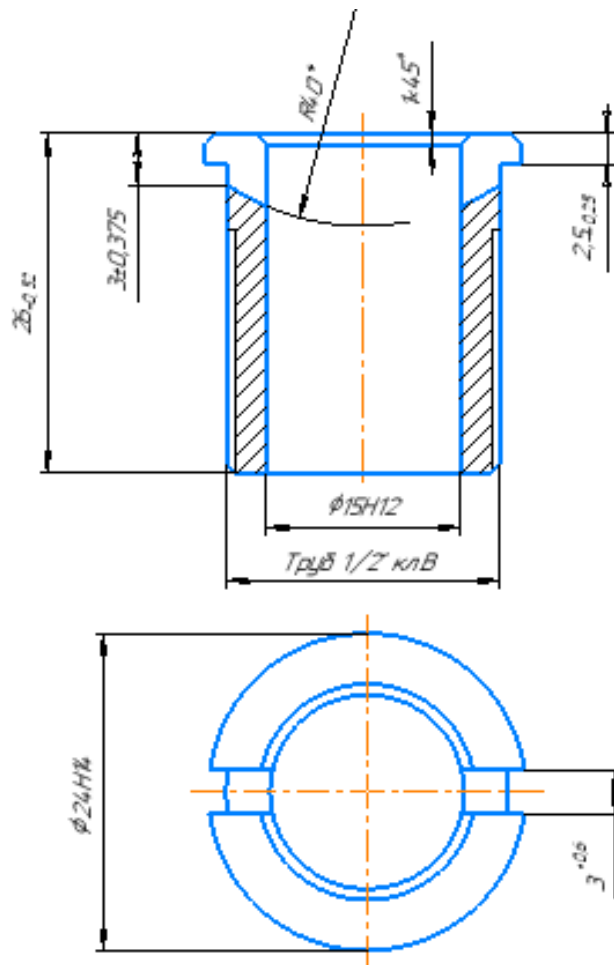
Загальний вигляд деталі «Втулка»
